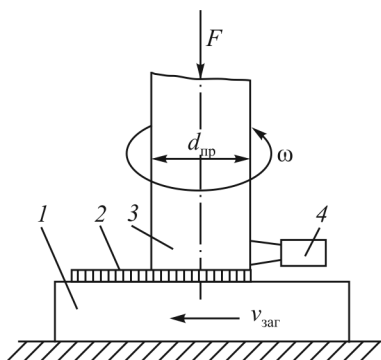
Схема наплавки трением: 1 – наплавленная поверхность; 2 – слой наплавленного металла; 3 – пруток; 4 – резец для снятия грата;  $d_{гр}$  – диаметр прутка
